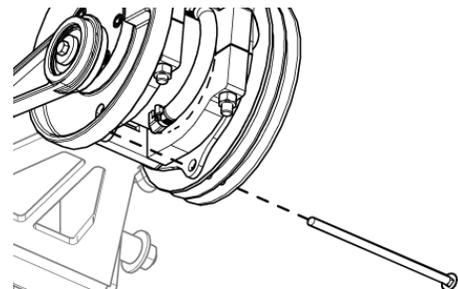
Ausrichten der Antriebsplatten mit einer Schraube
